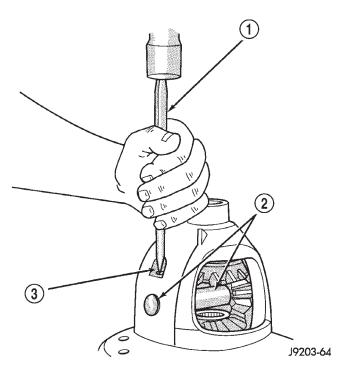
PASADOR DE RODILLO DEL EJE DE PIÑON ENGRANADO
